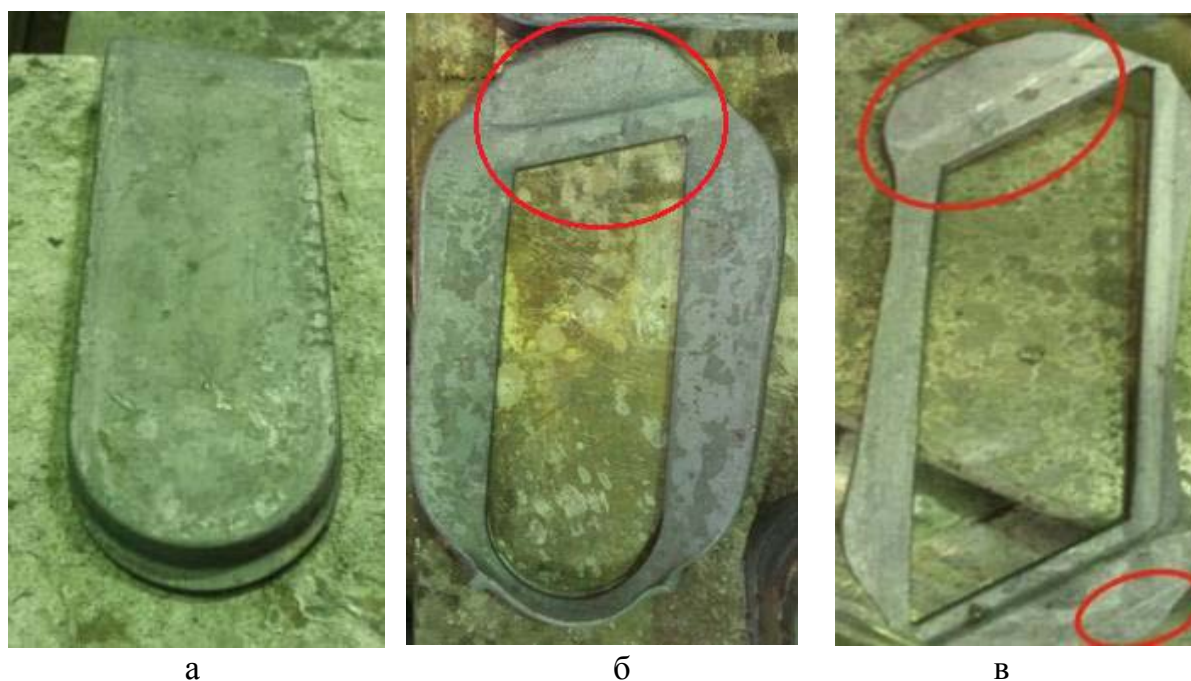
а – Штампованная заготовка с дефектом «ступень»
